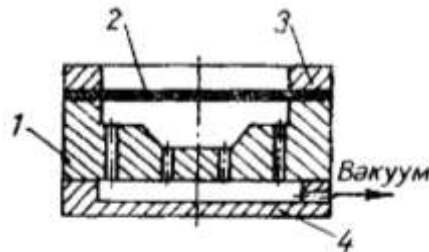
Схема вакуумного формування заготовок з листових пластмас: 1 – матриця; 2 – вихідна заготовка; 3 – притискне кільце; 4 – кришка
